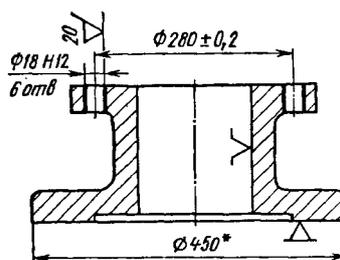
Фрагмент рабочего чертежа детали
